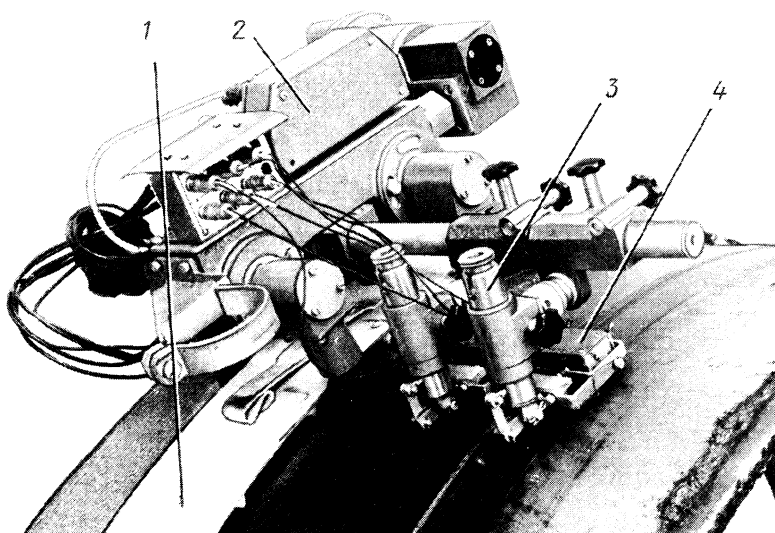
Полуавтоматическое устройство НК-143 "Спутник" для ультразвукового контроля кольцевых неповоротных сварных швов трубопроводов:
